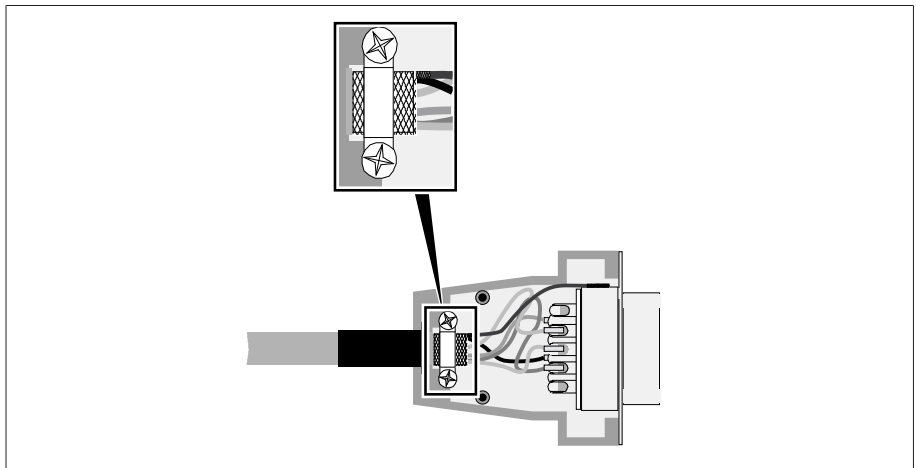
Exemple de blindage soudé au boîtier de connecteur
